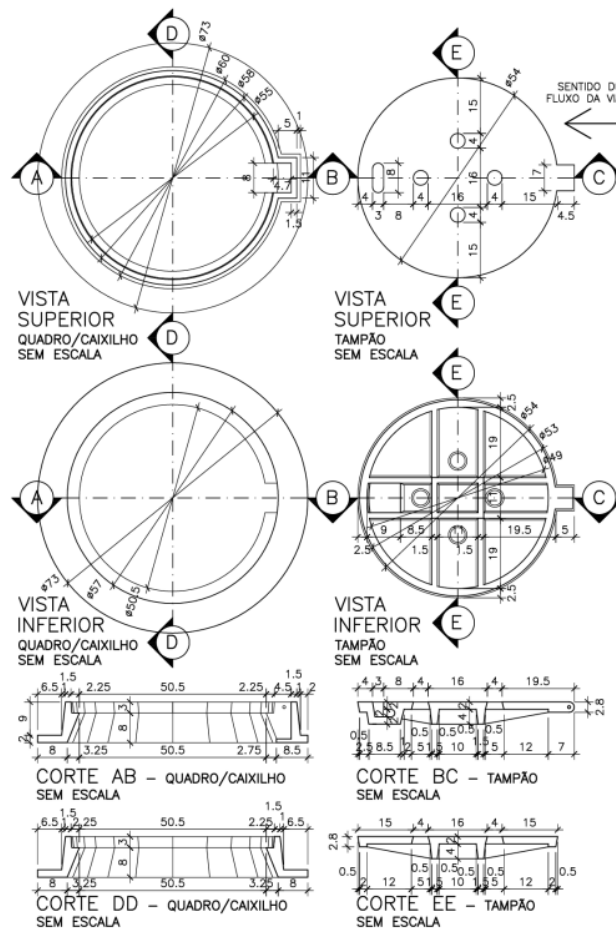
Tampão de Ferro Fundido Nodular – TFC
